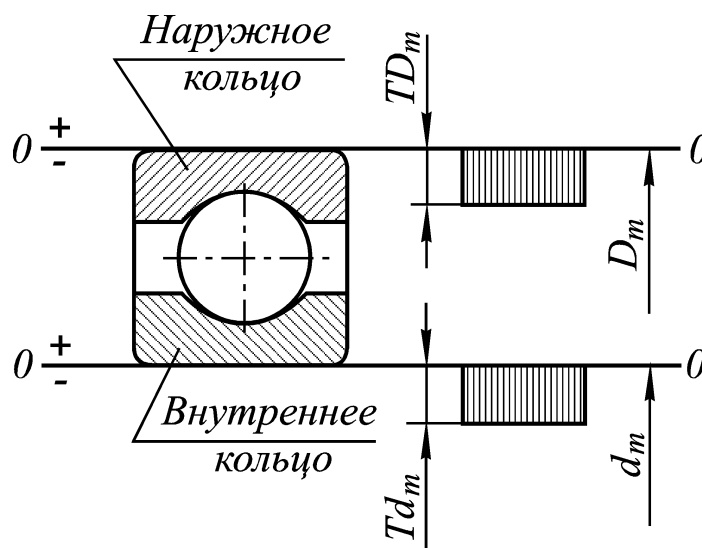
Расположение полей допусков посадочных диаметров колец подшипников
